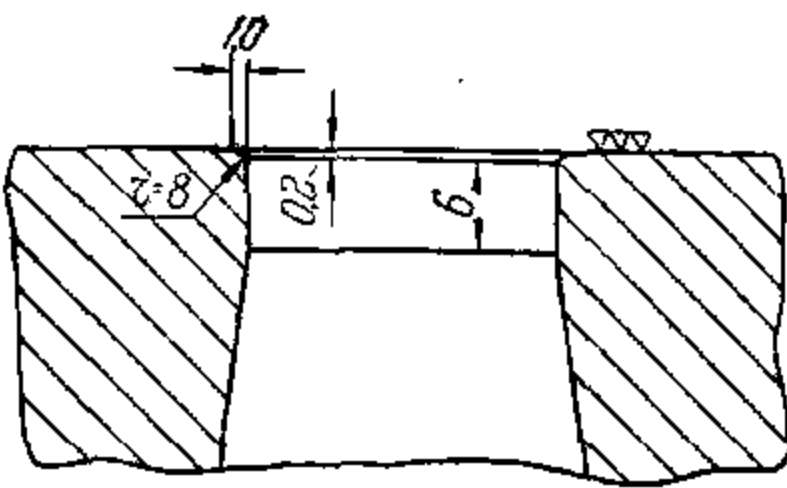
Чистовая вырубная матрица с закругленной режущей кромкой
